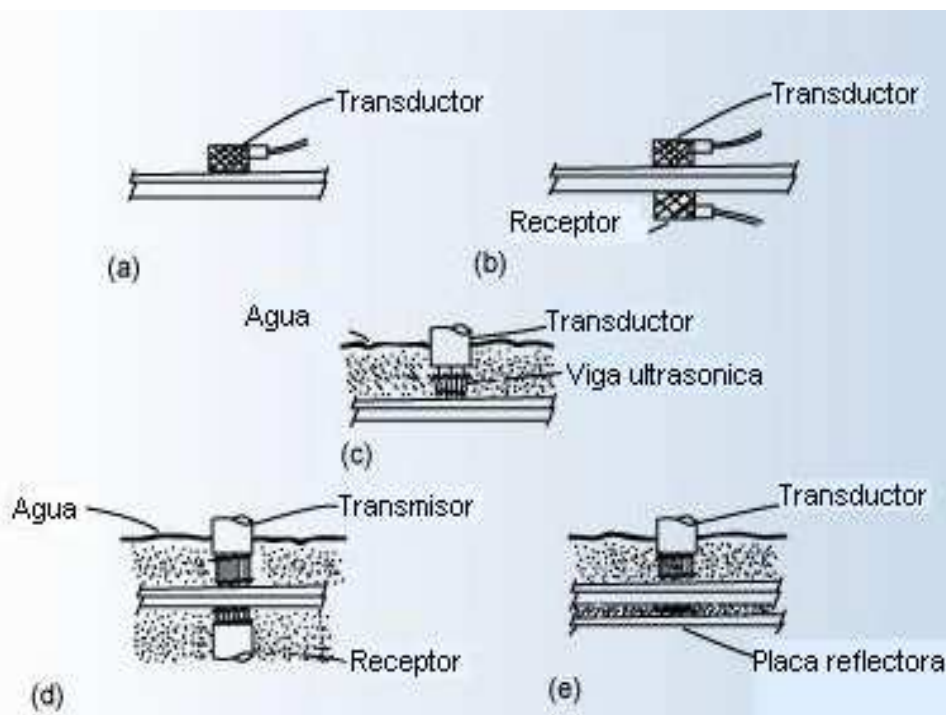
Técnicas de la inspección ultrasónica de END en adhesivos.
